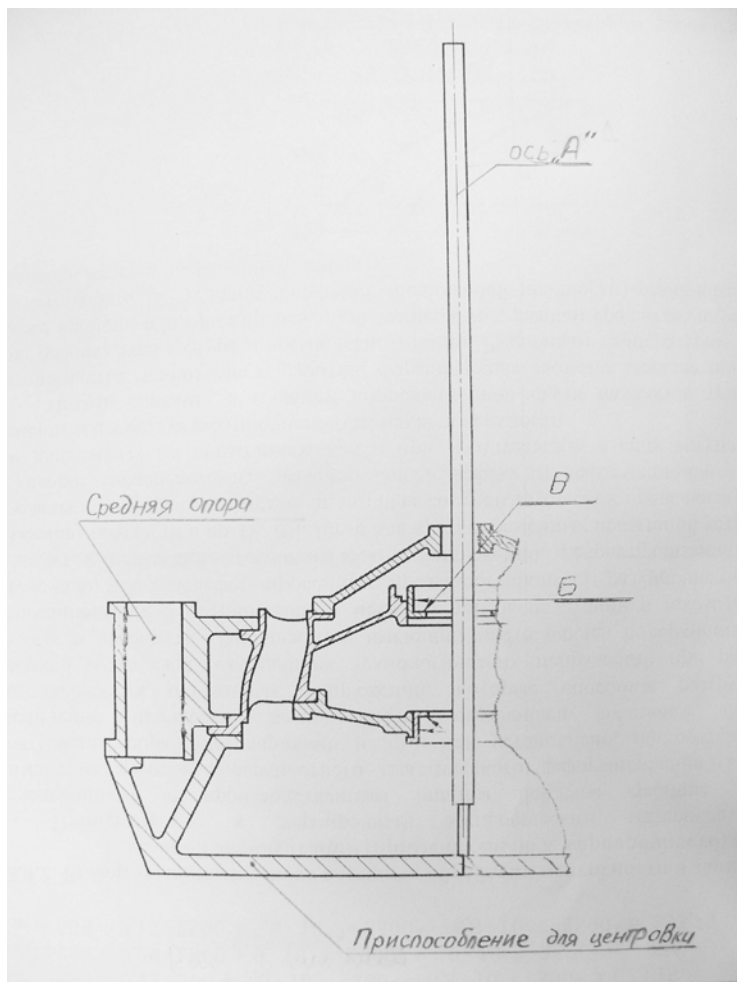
Средняя опора с приспособлением для центровки узлов.
